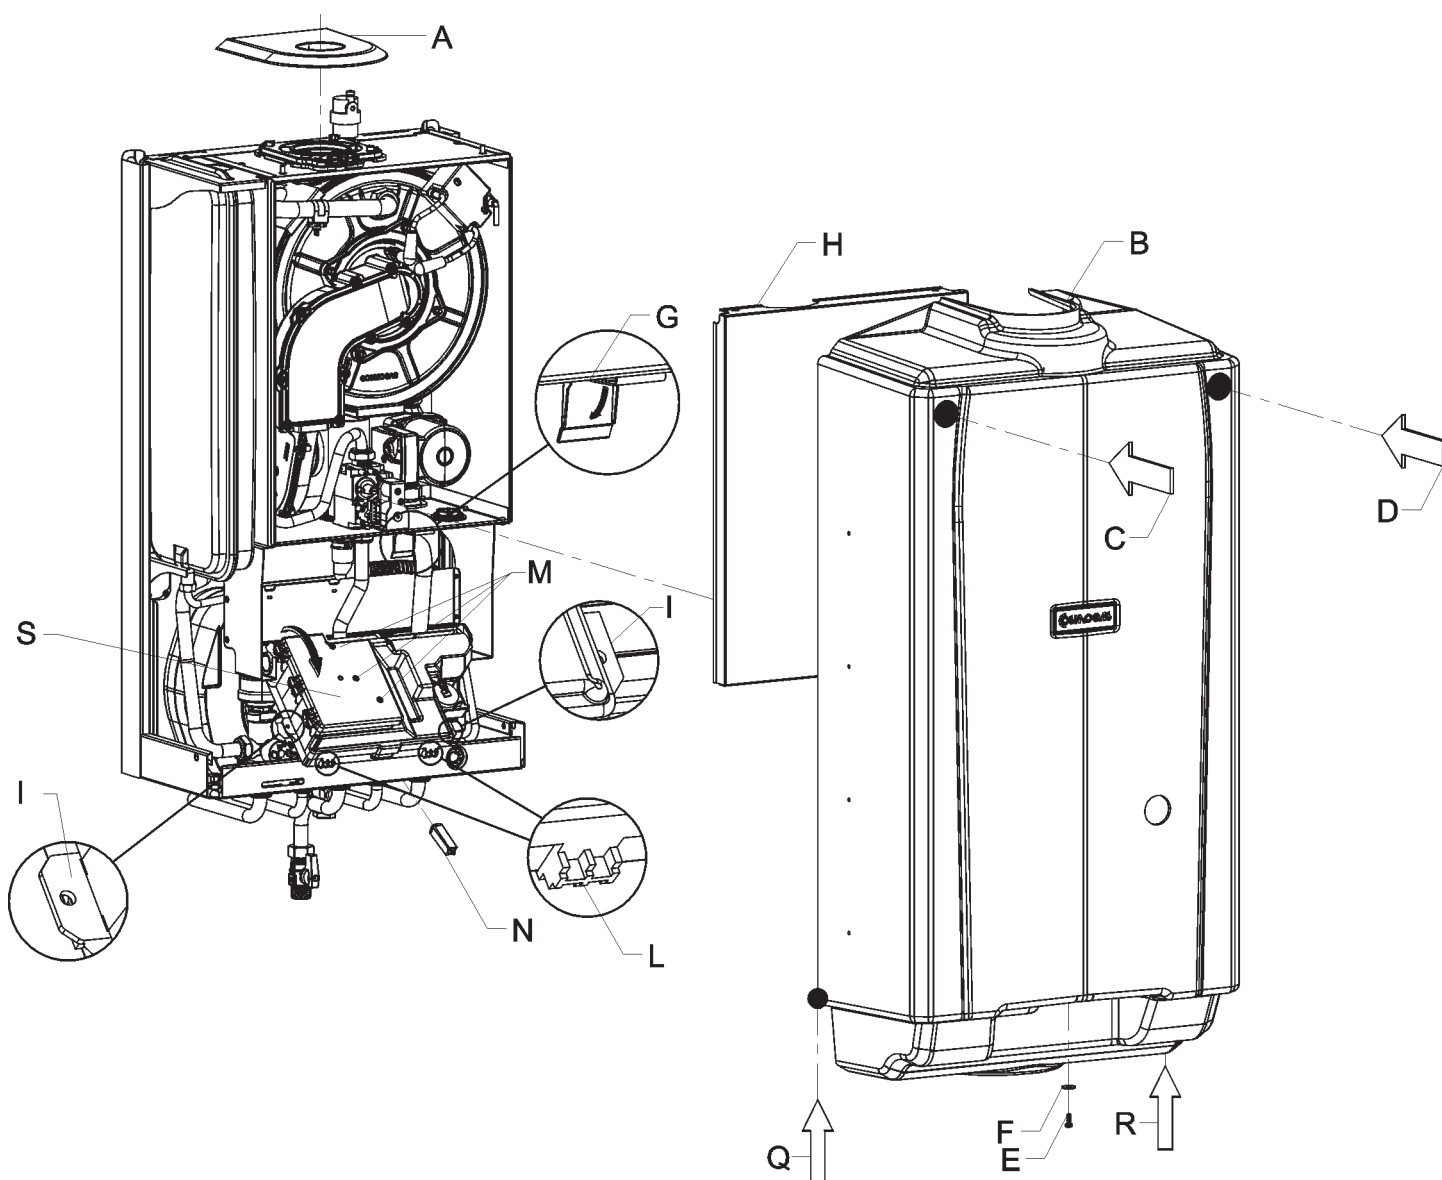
montaggio e smontaggio mantellatura e accesso componenti interni
